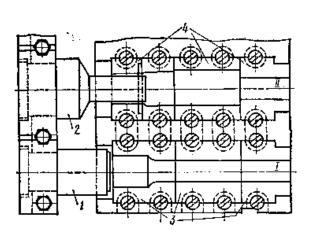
Схема штампа со сменными матричными вставками для высадки головки тяги обрезки облои:
